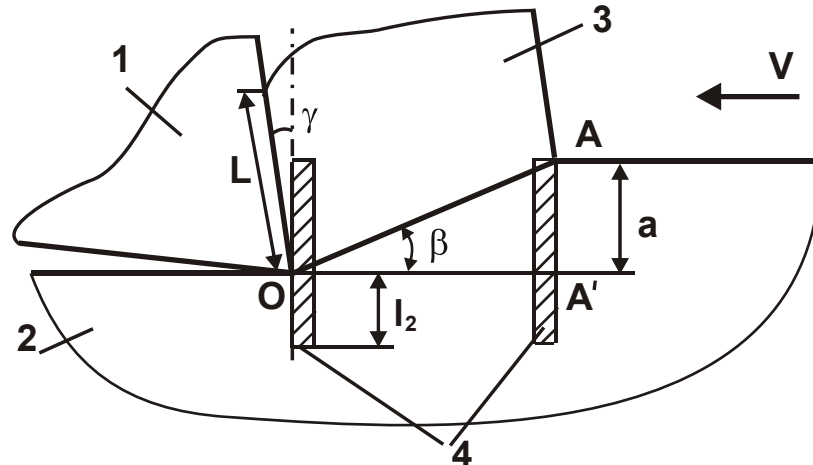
Расчетная схема процесса точения: 1 – резец; 2 – обрабатываемый материал; 3 – образующаяся стружка; 4 – адиабатический стержень
